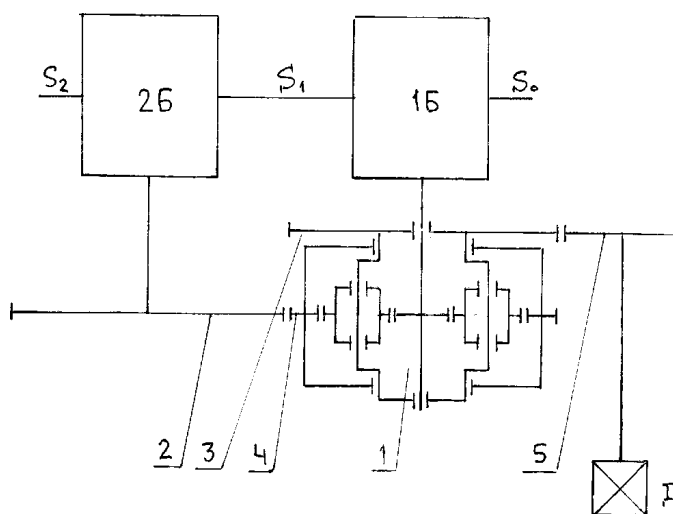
Адаптивная система трансмиссии привода тянущего устройства конвейера
